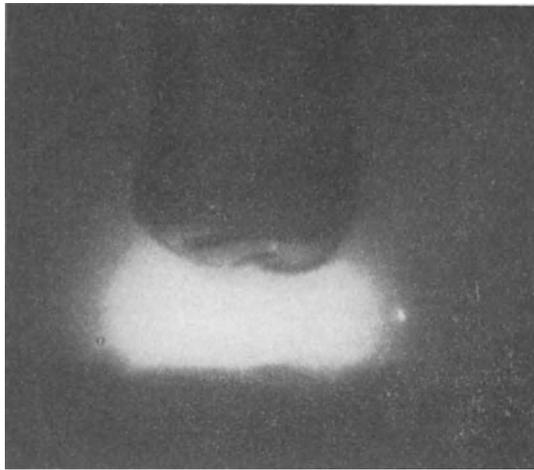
Photographische Aufnahme des Schweißlichtbogens einer nackten Elektrode von 4 mm \varnothing .
